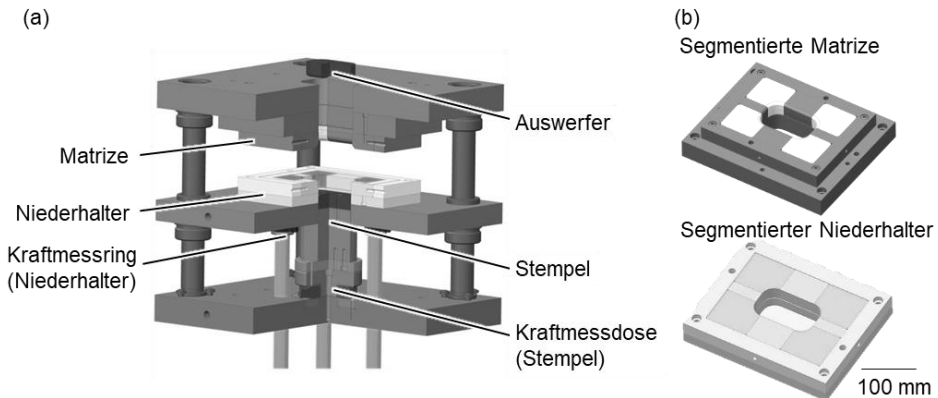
CAD-Modell des Gesamtwerkzeugs (a) und der Segmentierung (b)
